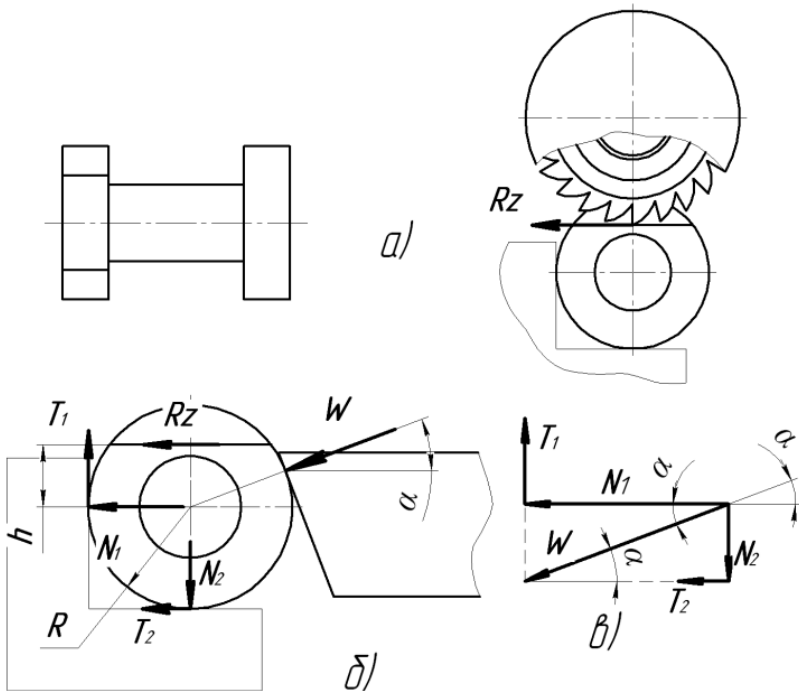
Схема сил при фрезеруванні лиски
